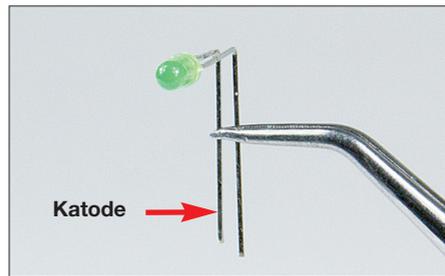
LED1 mit abgewinkelten Anschlussdrähten vor dem Einbau
